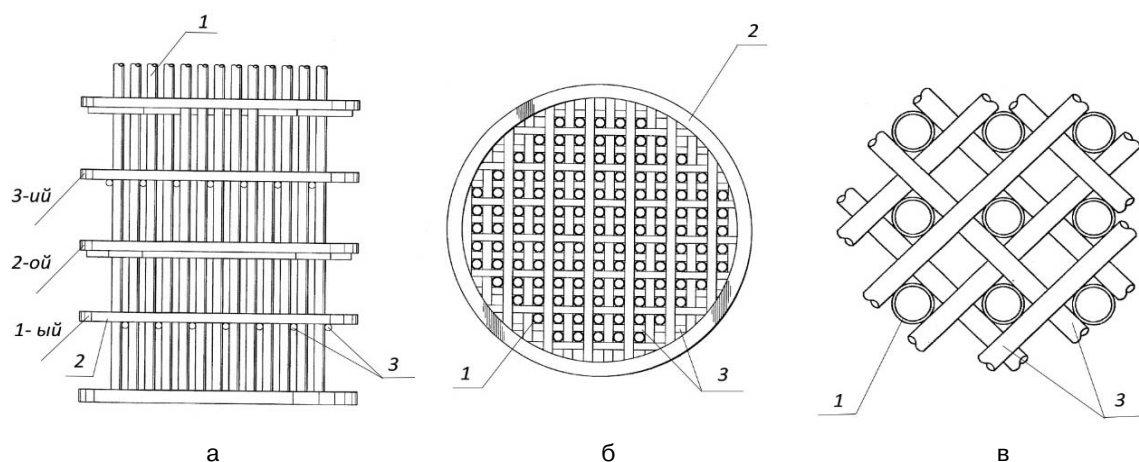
Стержневая опорная конструкция трубного пучка: а – вид сбоку на трубный пучок; б – разрез; в – взаимное расположение опоры и труб трубного пучка с размещением по вершинам квадрата; 1 – труба; 2 – опорное кольцо; 3 – круглые стержни
